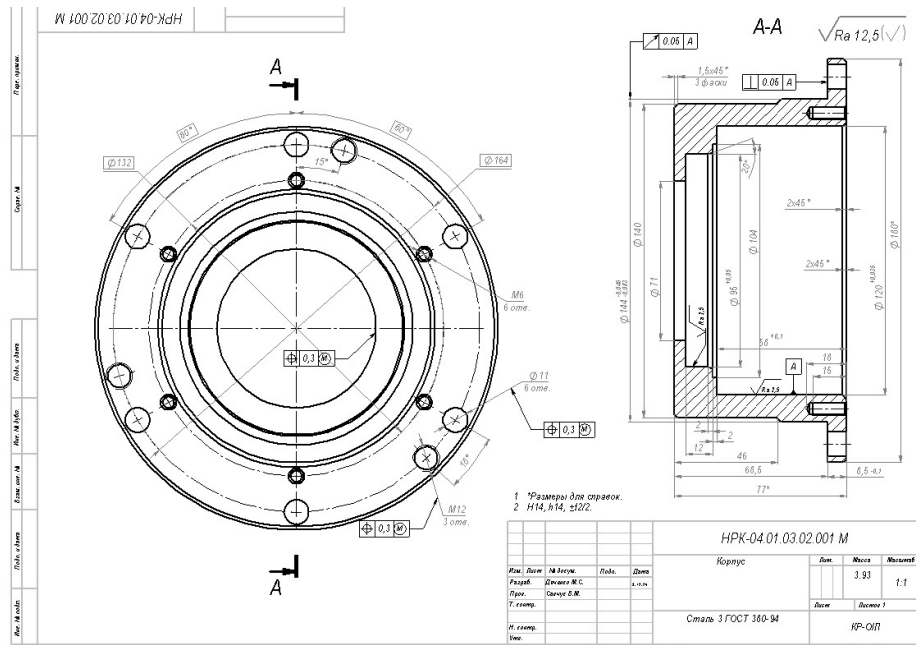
Креслення заданої деталі «Корпус подшипника»
